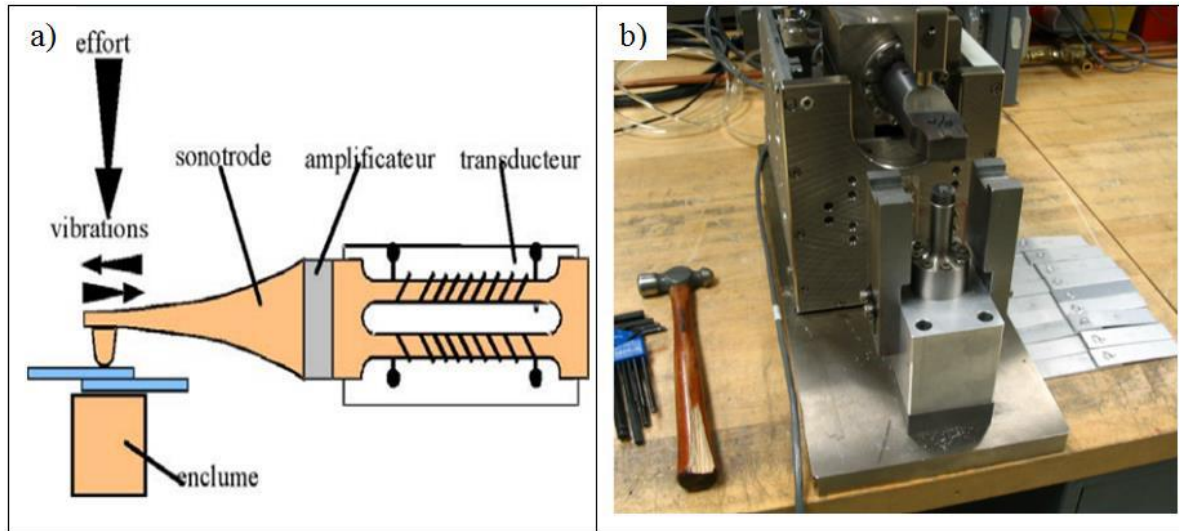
Soudage par ultrasons :a) schéma du procédé b) machine de soudage [4].
